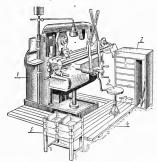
Рабочее место фрезеровщика: 1—станок; 2— инструментальный шкаф; 3— табурет; 4— подноживая решетия; 5— подставиа с ящиками для заготовок и деталой.
